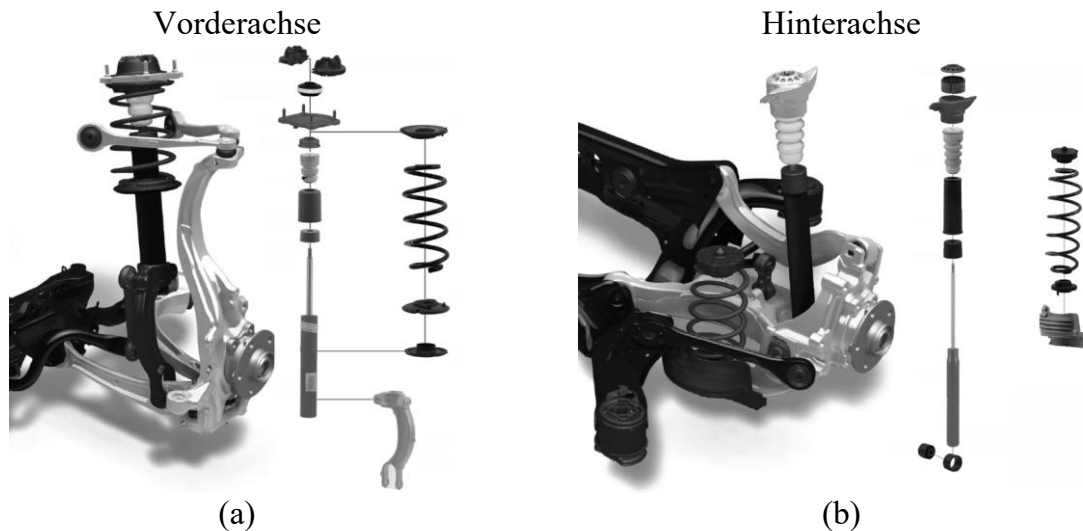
CAD-Modelle der linken Radaufhängungen der Vorderachse (a) und Hinterachse (b) mit Explosionsansicht der beiden Federungs- und Dämpfersysteme vom Referenzfahrzeug [166]
